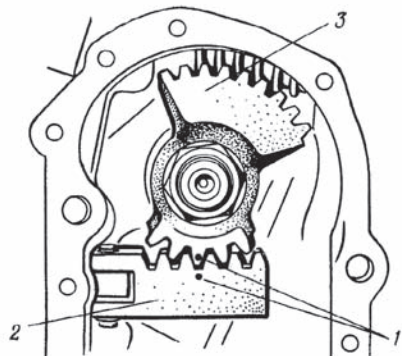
Совмещение меток рейки и сектора при установке поворотного вала. 1 — метки; 2 — рейка; 3 — сектор.
